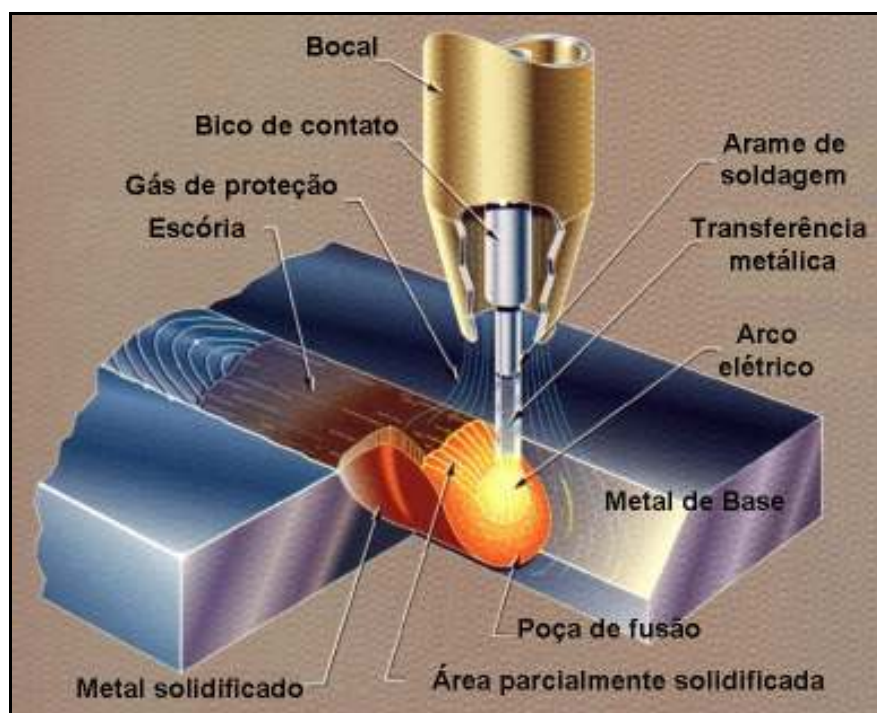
Processo de soldagem MIG/MAG (Costa, 2003).
